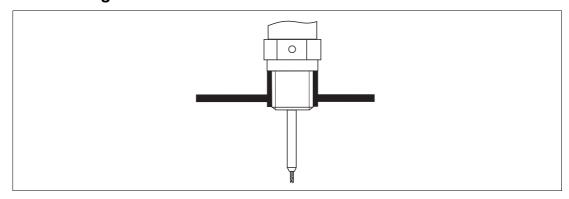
Montage mit Einschraubgewinde; bündig mit der Behälterdecke
